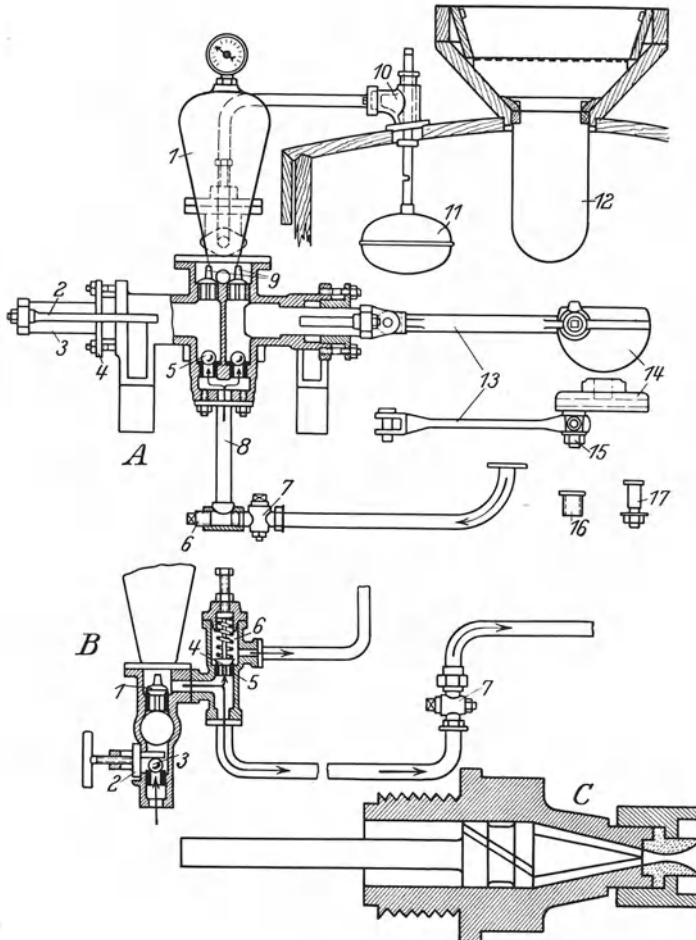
A* Längsschnitt von Pumpe und Behälter mit Sieb. Fahrbare Hederichspritze des KÄHLER-Typs. 1 Windkessel; 2 Verbindungsstange zwischen den Kolben; 3 Pumpenrohr; 4 Stopphahn; 5 kugelförmiges Saugventil; 6 Entleerungsventil; 7 Stopphahn; 8 Saugrohr; 9 kegelförmiges Druckventil; 10 Verbindungsstück des Reserveablaufrohres; 11 Schwimmer, der den Flüssigkeitsstand im Behälter angibt; 12 Untersieb aus Messing; 13 Pumpenstange; 14 Kurbelwellenscheibe; 15 und 17 Kurbelwelle; 16 Kurbelwellenlager. *B* Querschnitt der Pumpe und des Sicherheitsventils des KÄHLER-Typs. 1 Druckventil; 2 Deckel des Ventilgehäuses; 3 Saugventil; 4 Feder des Sicherheitsventils; 5 kegelförmiges Sicherheitsventil, das mit Hilfe einer Feder und einer Einstellungsschraube in Stellung gehalten wird; 6 Ventilgehäuse; 7 Stopphahn des Verteilerrohres. *C* Zerstäuberdüse der Hederichspritze.
